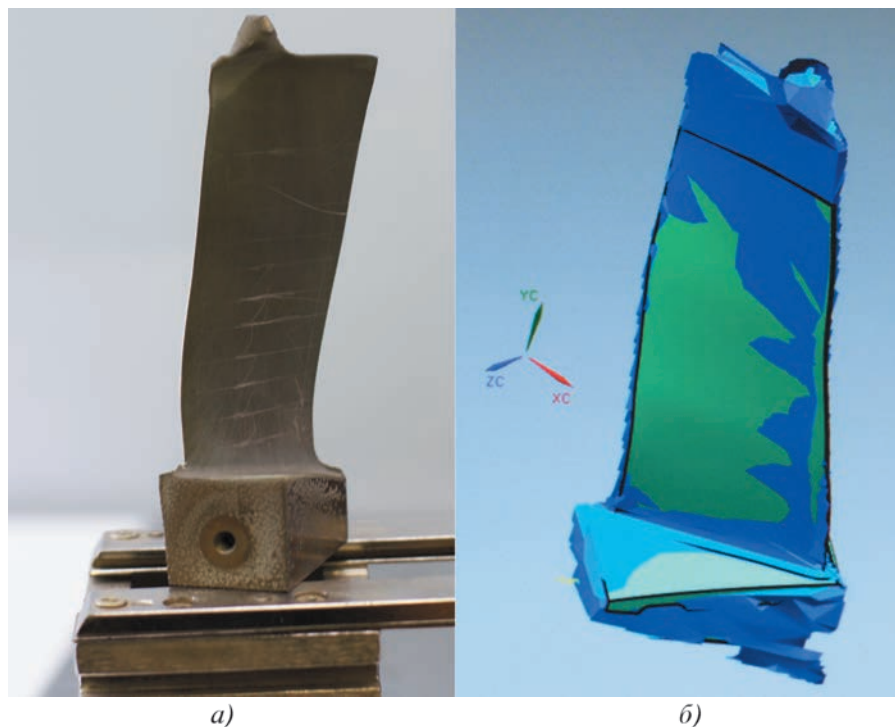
Измеряемая заготовка — лопатка компрессора ГТД (а) и результат совмещения синтезированной векторно-растровой модели с исходной математической моделью заготовки (б)
